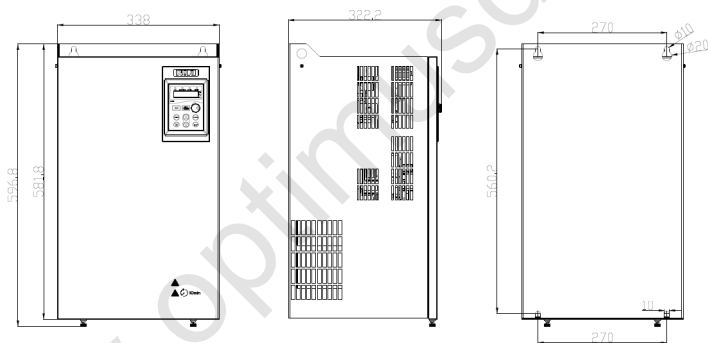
Габариты и монтажные размеры ПЧ 75-110 кВт
